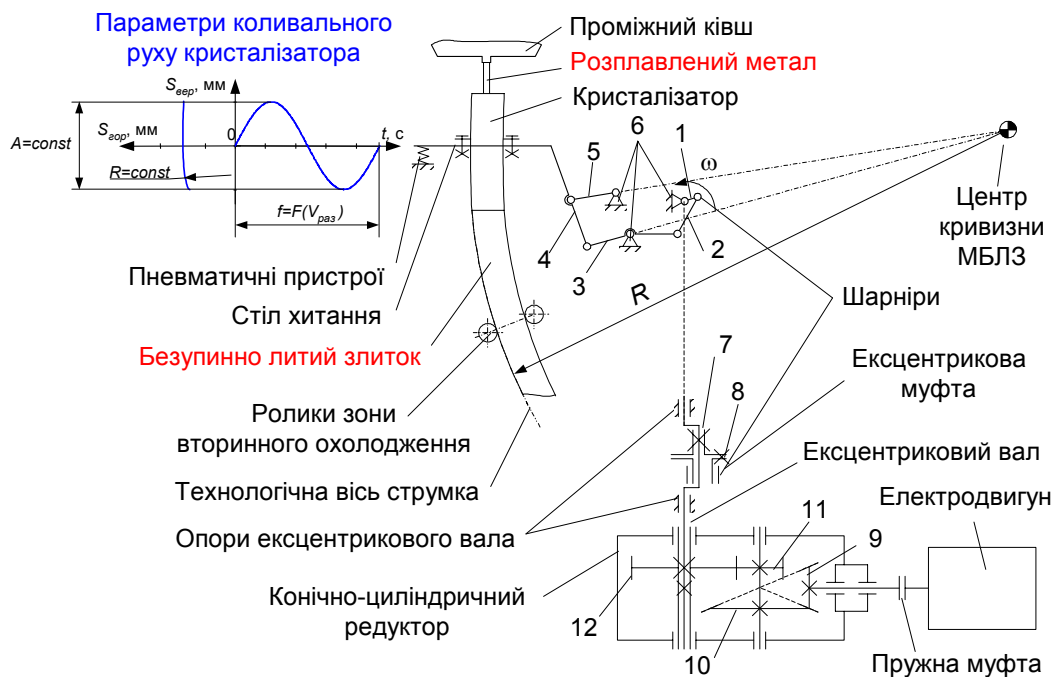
Кінематична схема механізму хитання кристалізатора МБЛЗ
